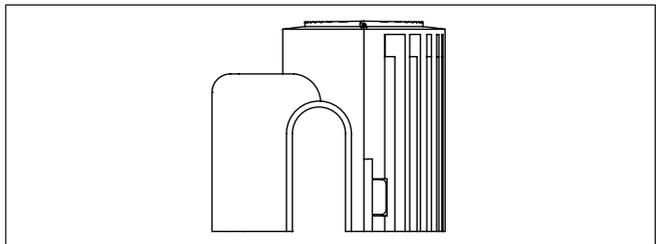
Cubierta protectora para caja con conexión de cables tangencial
